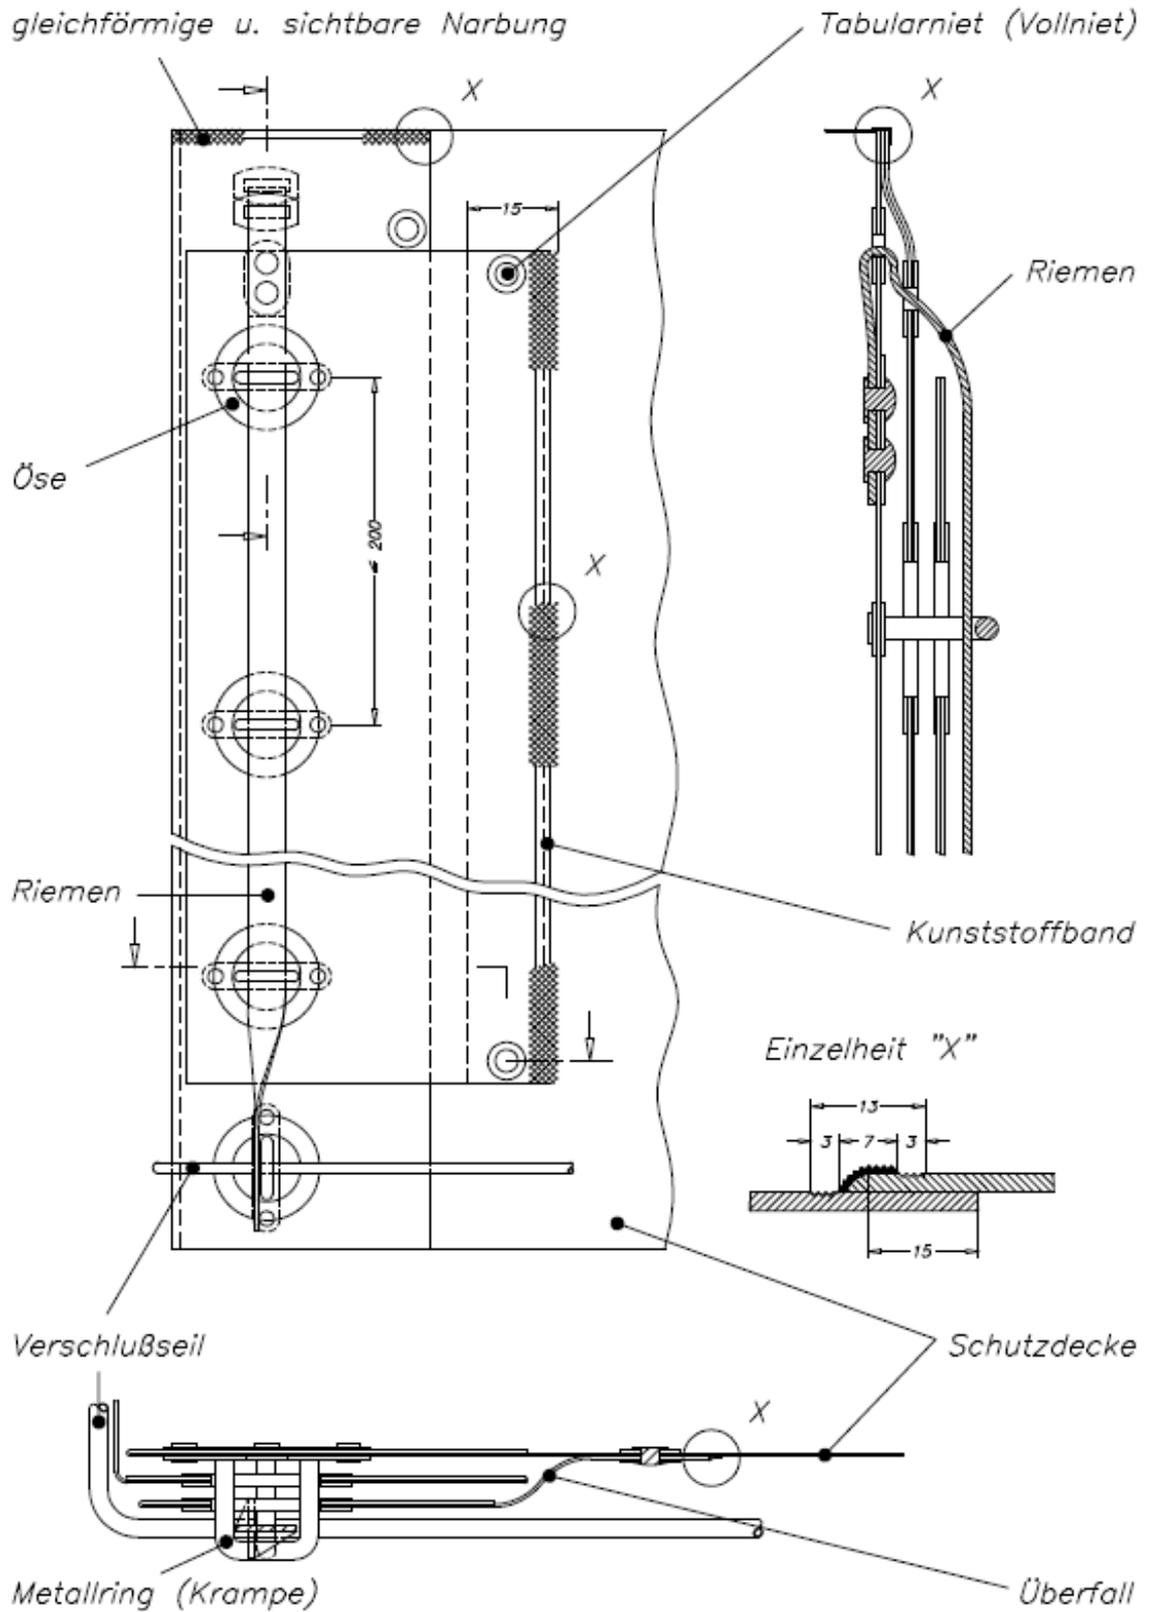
Öffnung an der Schutzdecke (Ecken)
